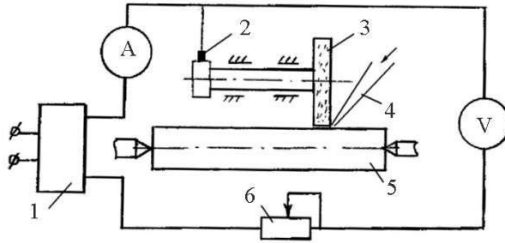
Схема електрохімічного шліфування: 1 – випрямляч; 2 – ковзний контакт; 3 – струмопровідний круг; 4 – електроліт; 5 – оброблювана деталь; 6 – реостат
